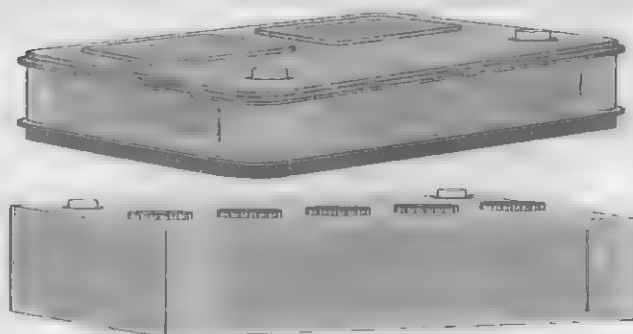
Крышки батарей со снимаемыми крышками или планками
